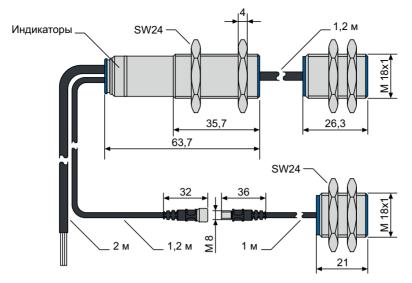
Габаритные размеры датчиков dbk+4/M18/...
